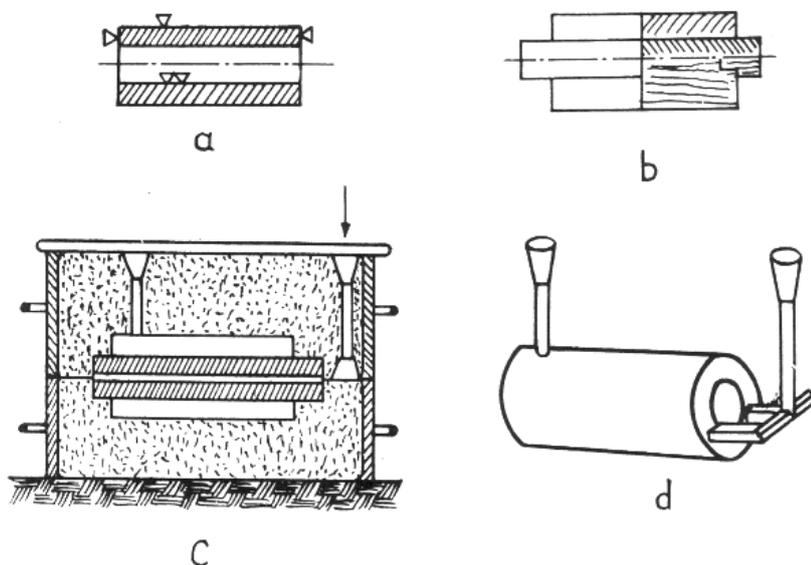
Moldeo con macho de un tubo. a) Plano de la pieza, b) modelo y macho, c) molde preparado para la colada, d) pieza sin desbarbar.
